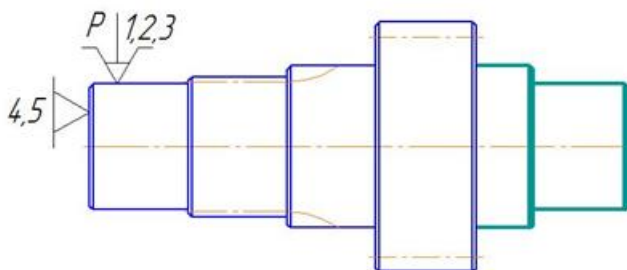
Схема базування та закріплення заготовки на операцію
